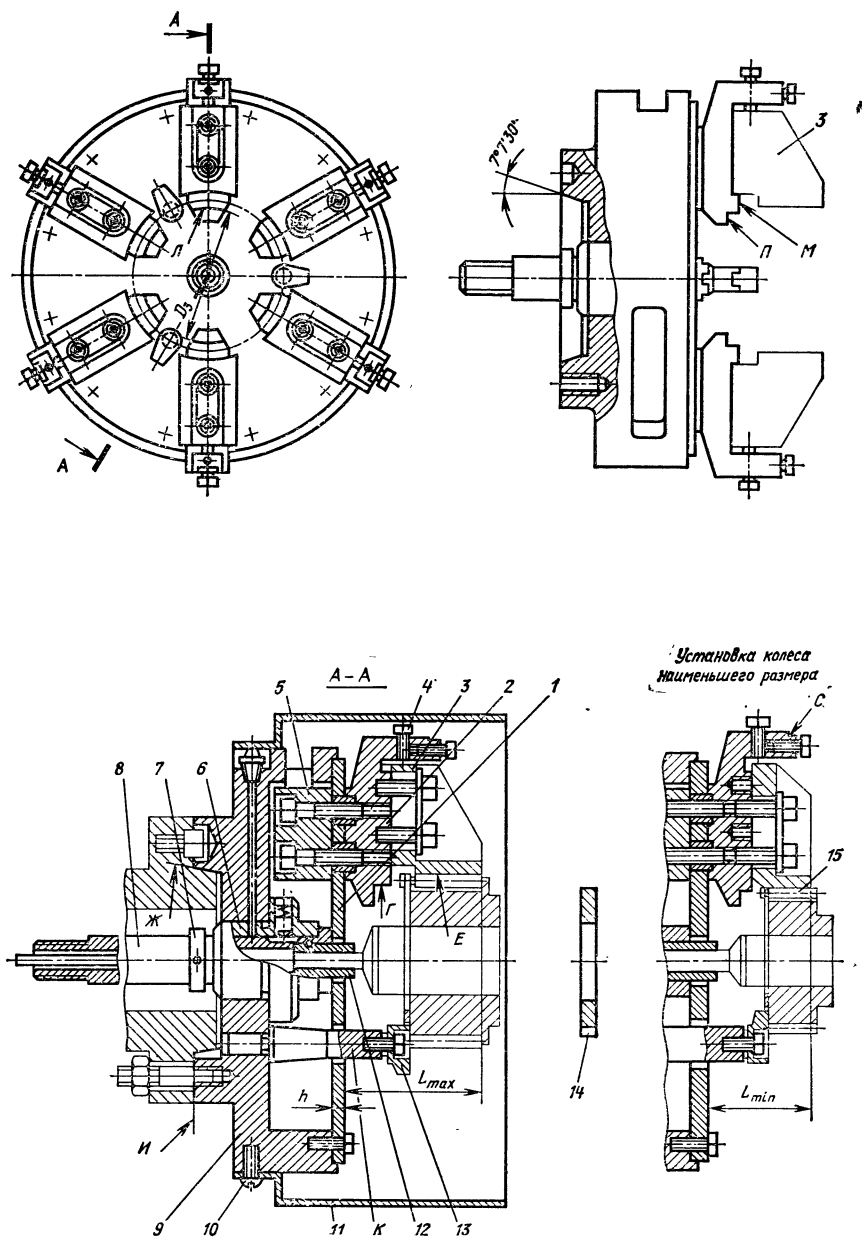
Специализированный наладочный мембранный патрон для шлифования отверстий в зубчатых колесах
